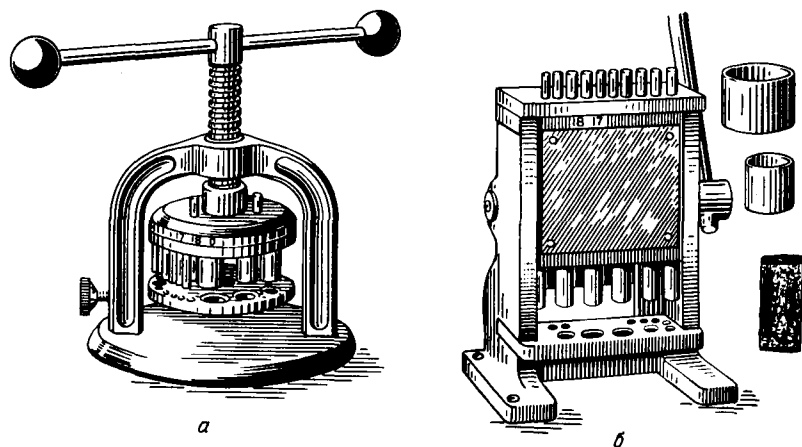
Аппараты Шарпа (а) и «Самсон» (б) для получения и подготовки металлических гильз.
